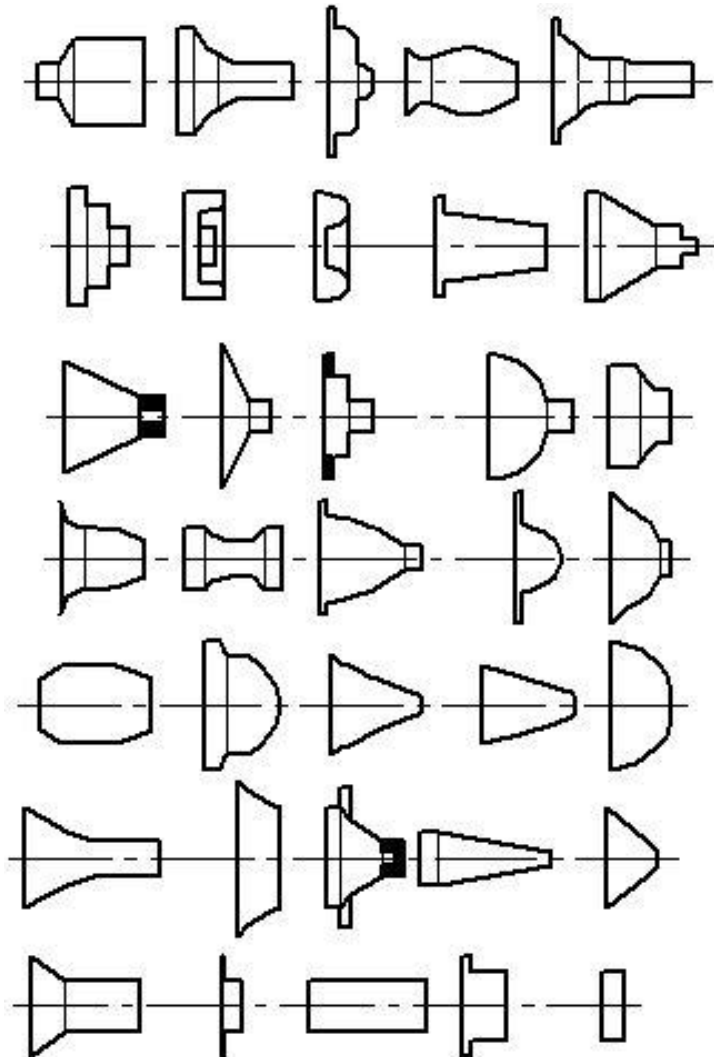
Деталі, що виготовляються ротаційної витяжкою
